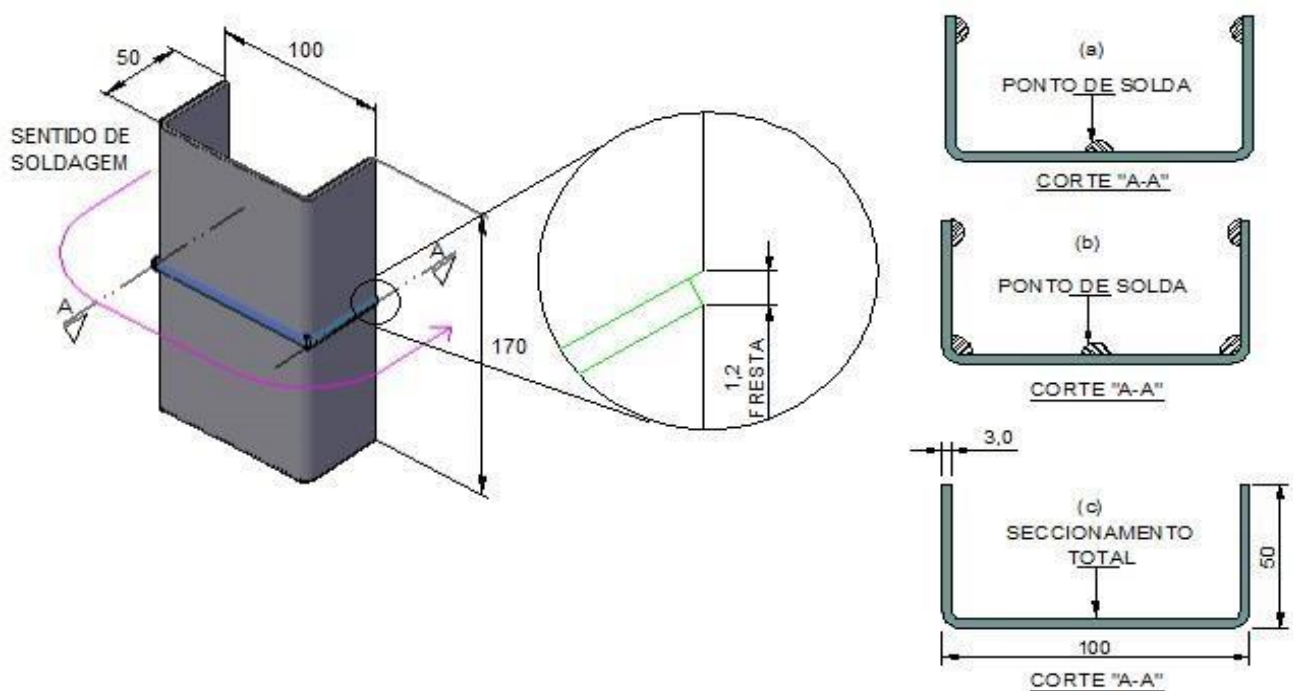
Montagens das juntas para a soldagem: (a) com três pontos de solda; (b) com cinco pontos de solda; (c) e seccionamento total.
